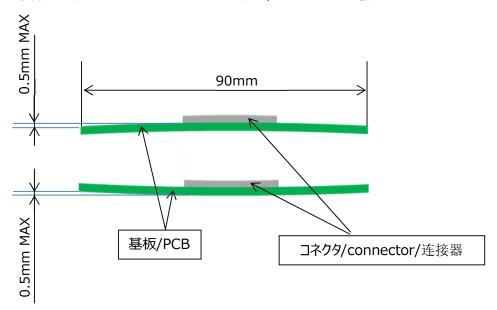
基板反り量 / Fig.23 Amount of PCB warp / 图 23.PCB 变形量
